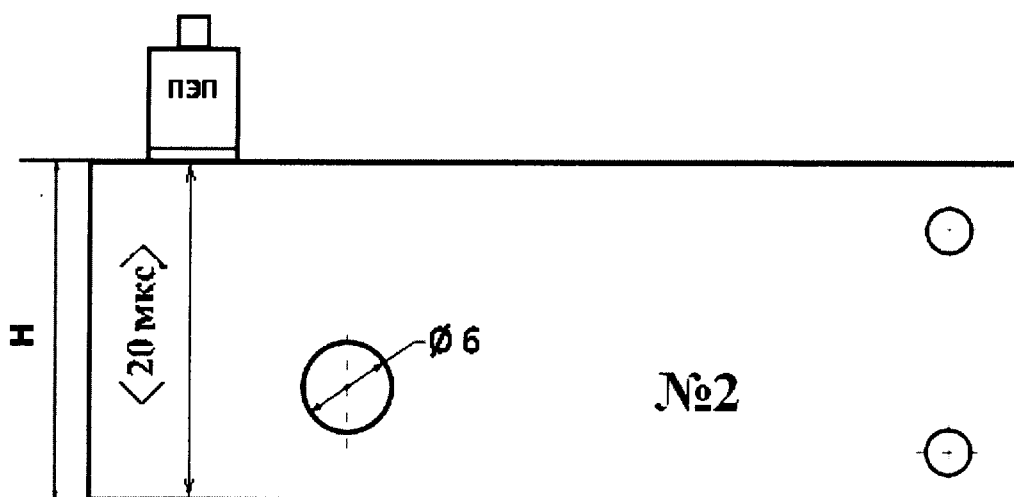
Контрольный образец №2 из комплекта КОУ-2
